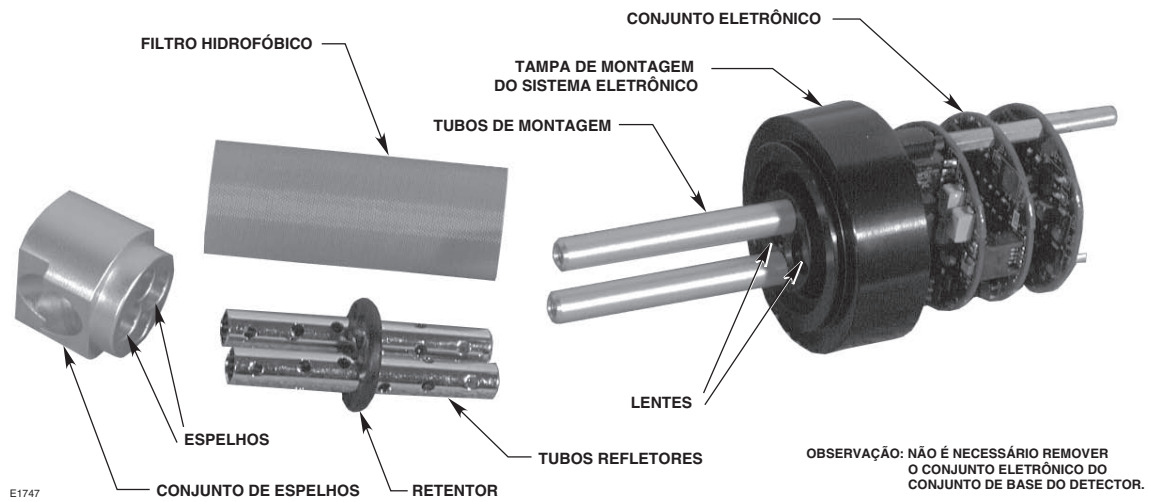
Desmontagem para limpeza do detector PIR9400 de alumínio
